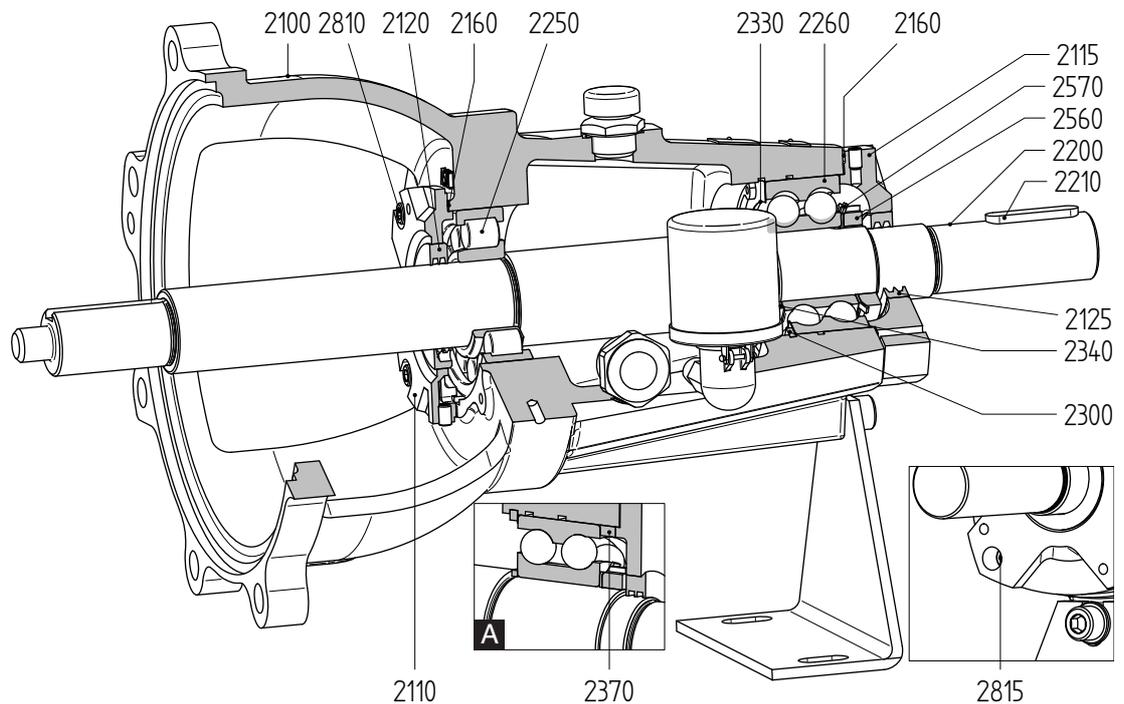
Подшипник L4 (усиленный, с масляной смазкой) (A = группа подшипников 3)
